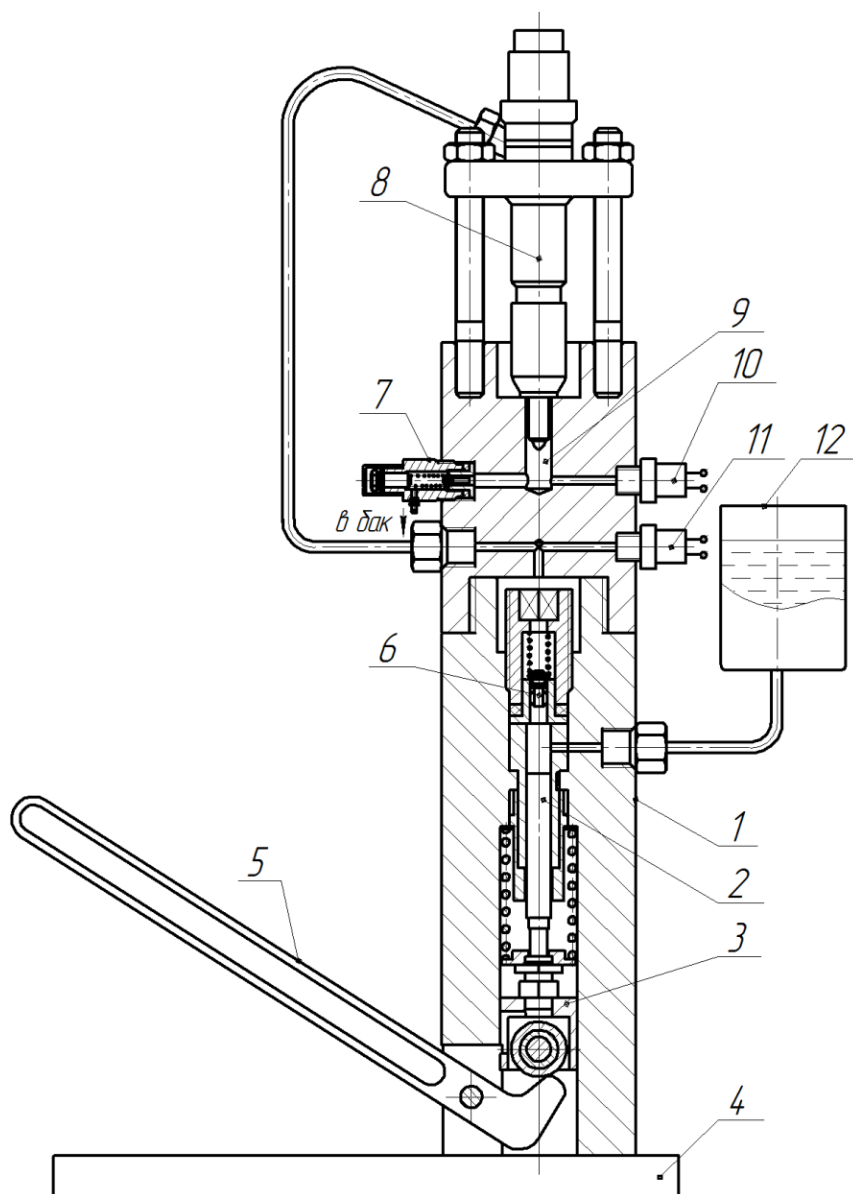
Стенд с противодавлением впрыску для регулировки форсунок: 1- корпус; 2- насосный элемент; 3- толкатель; 4- плита опорная; 5- рычаг; 6- нагнетательный клапан; 7- клапан противодействия; 8- форсунка; 9- камера впрыска; 10, 11- датчики давления типа МД; 12- топливный бачок
